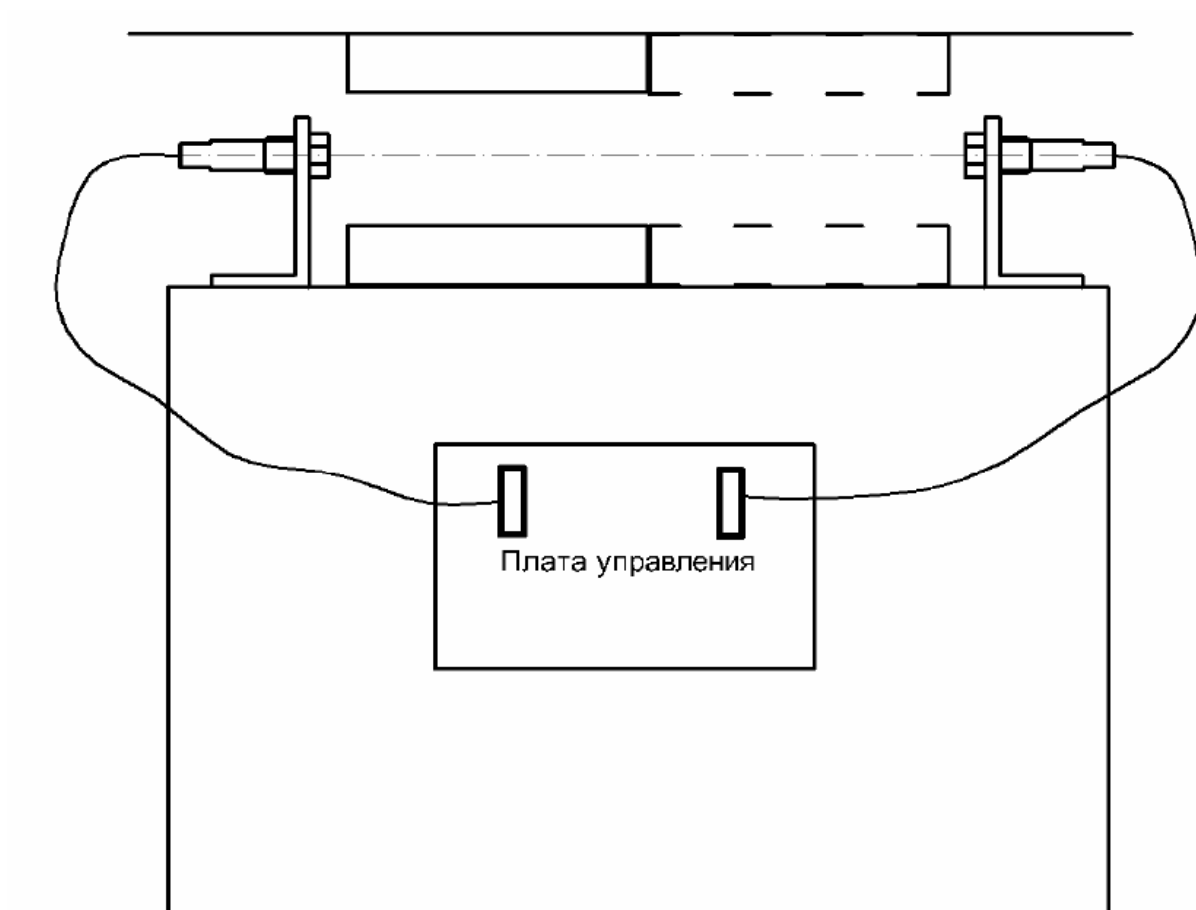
Установка излучателя и приемника на кабине (вид сверху)
